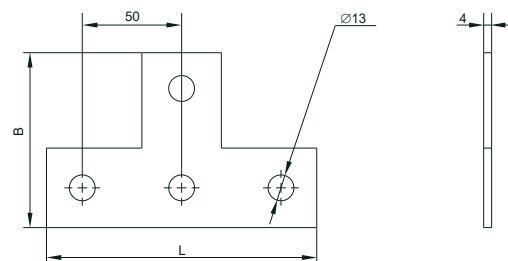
Пластина соединительная Т-образная для STRUT-профиля / Figure I.3 – T-shaped joining plate for STRUT profile
